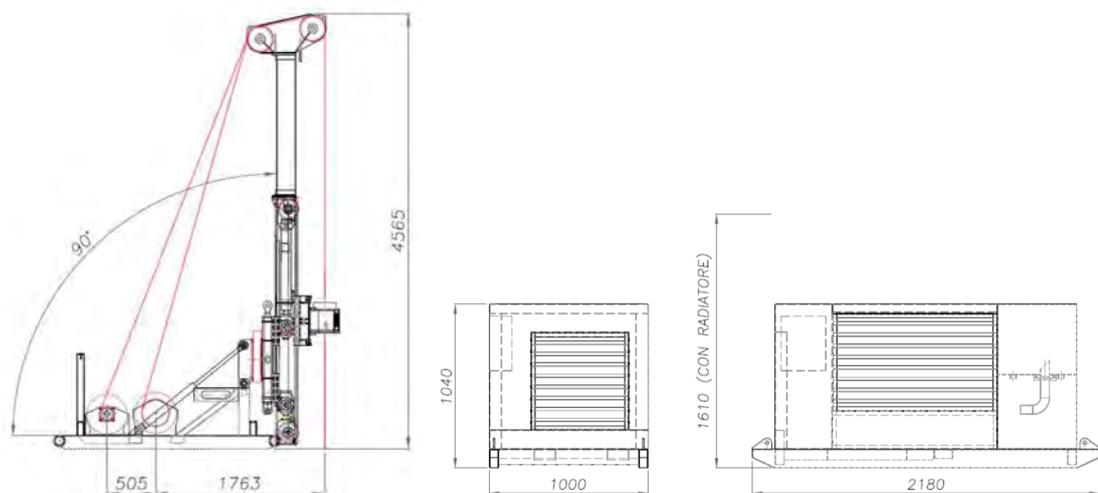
Vista schematica Stazione di sondaggio modulare con centralina diesel idraulica insonorizzata
